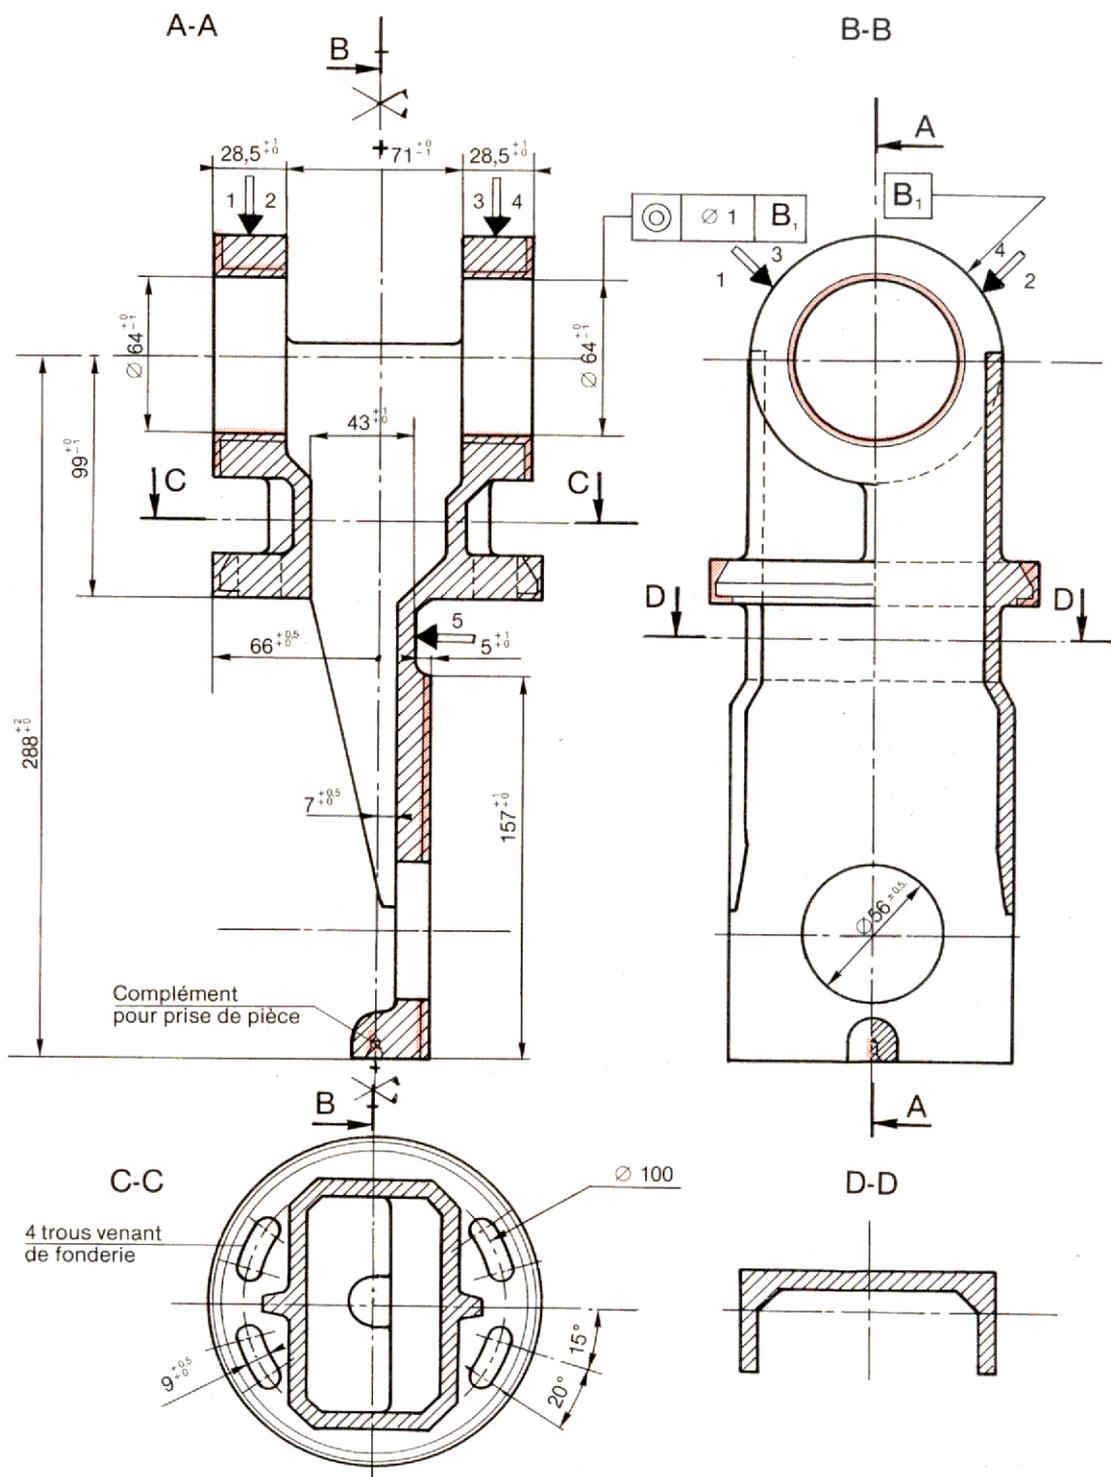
Exemple de projet de dessin de pièce moulée étudiée par le BE.
